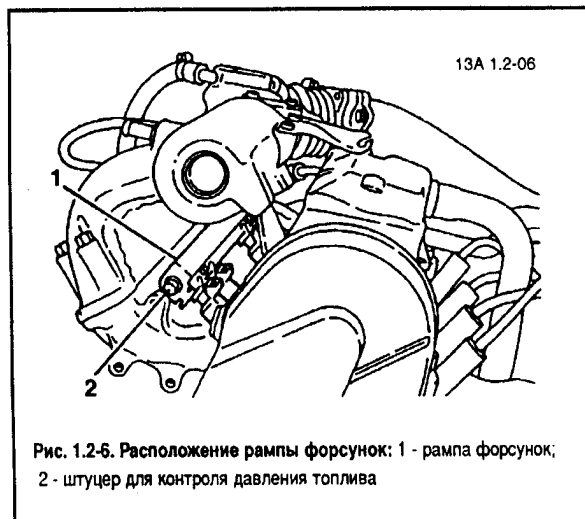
Расположение ramпы форсунок: 1 - ramпа форсунок; 2 - штуцер для контроля давления топлива
